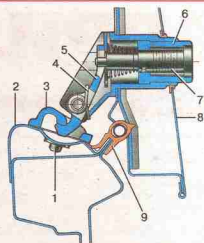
Замок двери задка: 1 – болт крепления фиксатора; 2 – пружина крючка; 3 – фиксатор; 4 – пружина крючка; 5 – крючок; 6 – корпус замка; 7 – цилиндр привода замка; 8 – дверь задка; 9 – уплотнитель проема двери
